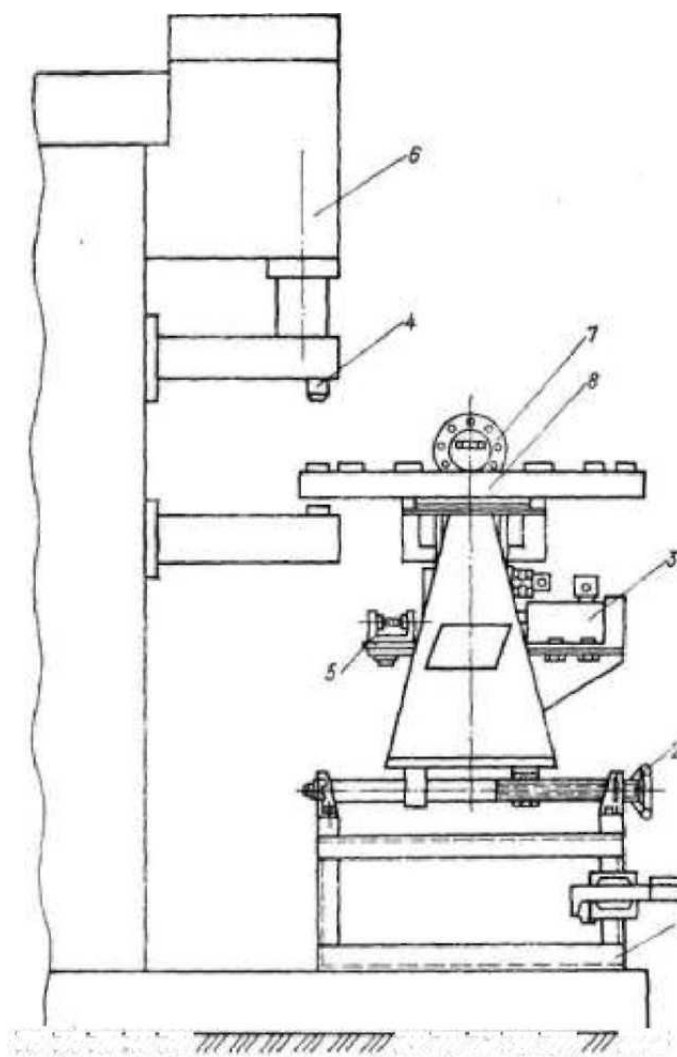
Установка для контактной сварки с многопозиционным поворотным столом
